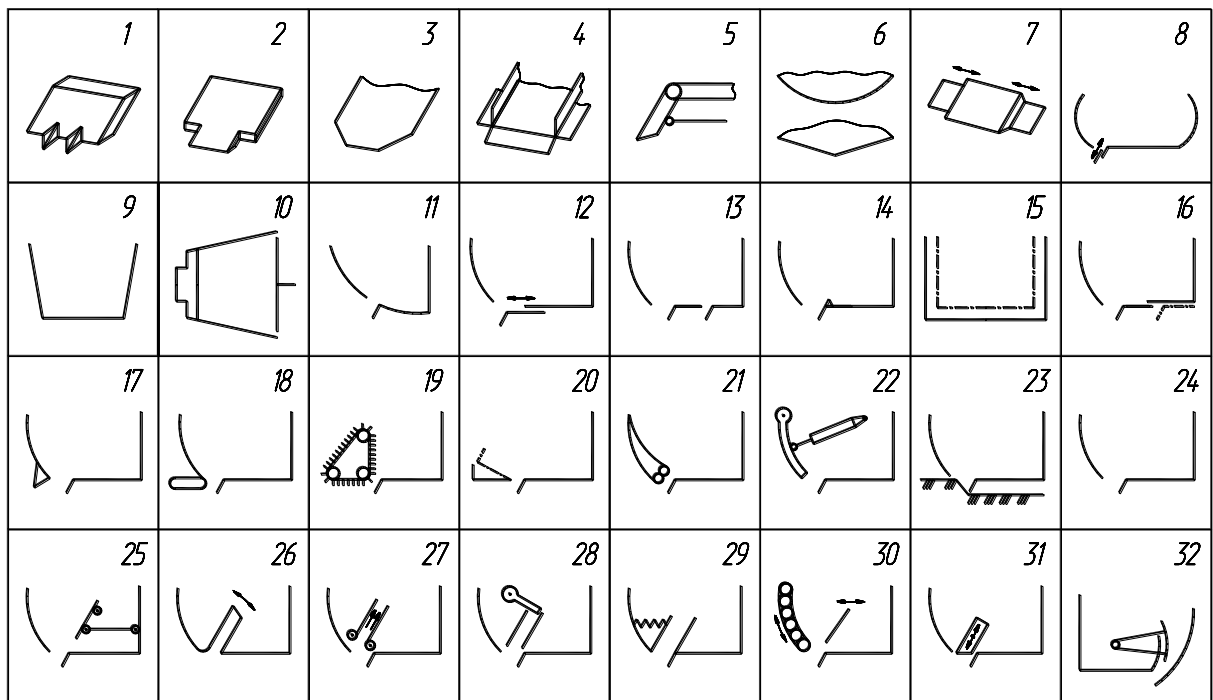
Схеми інтенсифікації робочого процесу скреперів: 1 - зубчасті ножі; 2 - виступаючі ножі; 3 - косопоставлені бокові ножі; 4 - прямий совок; 5 - поворотний ніж; 6 - фігурні ножі; 7 - ножі, які змінюються по ширині; 8 - вібруючий ніж; 9 - ківш з похилими боковими стінками; 10 - ківш з поворотом бокових і задньої стінок; 11 - ківш з криволінійним днищем; 12 - телескопічний ніж; 13 - ківш з двошліпінним завантаженням; 14 - ківш з направляючою на днище; 15 - ківш з антифрикційним покриттям; 16 - ківш з рухомим днищем; 17 - заслінка з опорною лижею; 18 - заслінка з стрічковою опорою; 19 - заслінка з опорою у вигляді скребкового транспортера; 20 - горизонтальна ковзаюча заслінка; 21 - заслінка з механізмом сколу; 22 - підгірбаючий пристрій; 23 - заслінка з винесенням за призму волочіння; 24 - глибока заслінка; 25 - направляюча плита; 26 - з ґрунтоводом, який відхиляється; 27 - віброконвеєр; 28 - ґрунтовід з повітряним змащенням; 29 - ківш з роздільним наповненням ковша; 30 - механізм обтискування стружки в ковші; 31 - відвальна стінка з рухомою заслінкою; 32 - ґрунтонаправляючий пристрій
